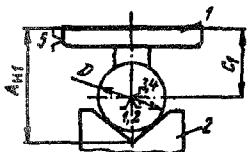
Схема размерной настройки с погрешностью схемы базирования:
